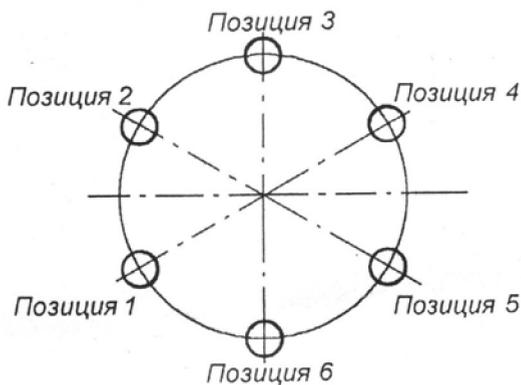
Схема смены позиций заготовки на многошпиндельном станке
